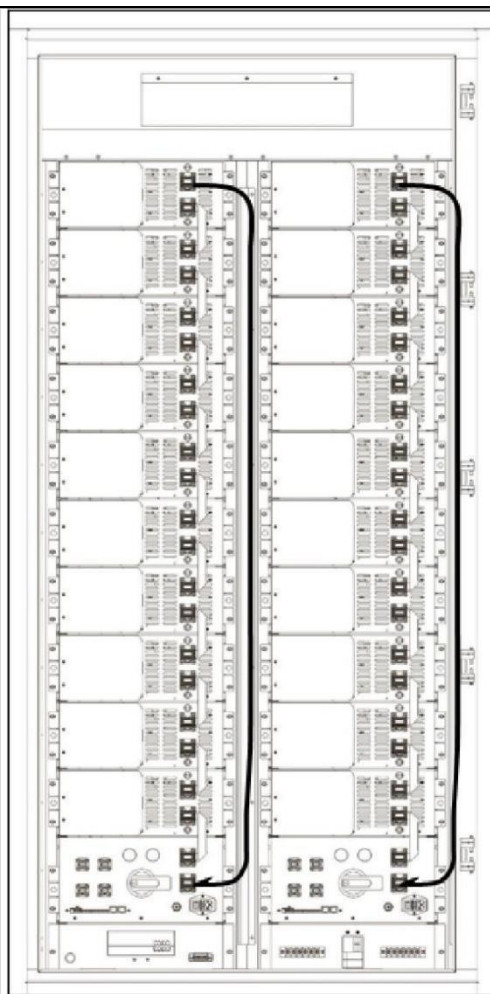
Collegamento del cavo di alimentazione "B-".
